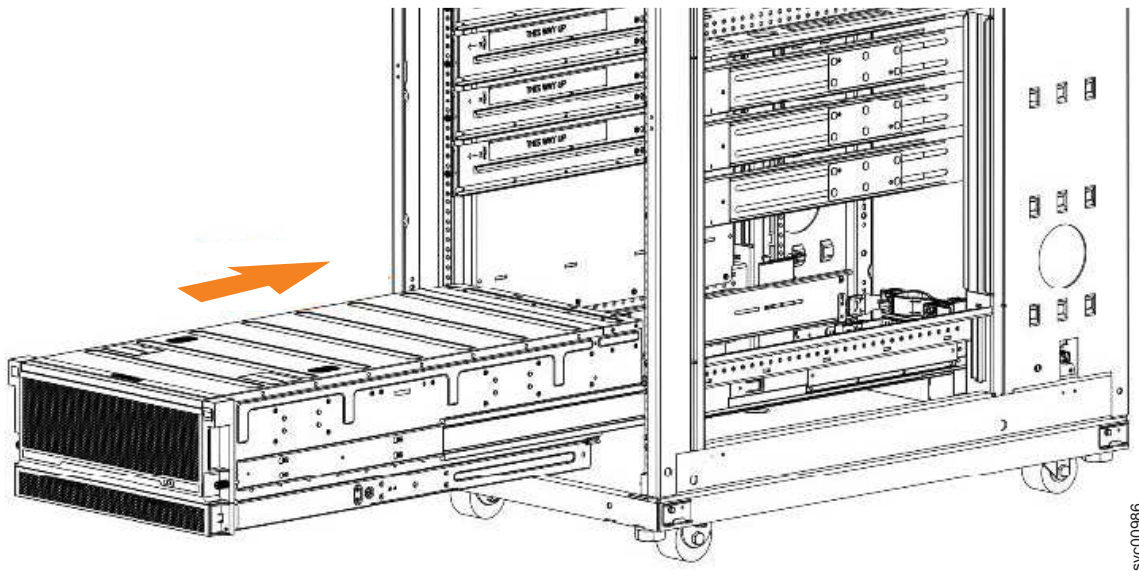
Gehäuse in Rack installieren (Beispiel)
